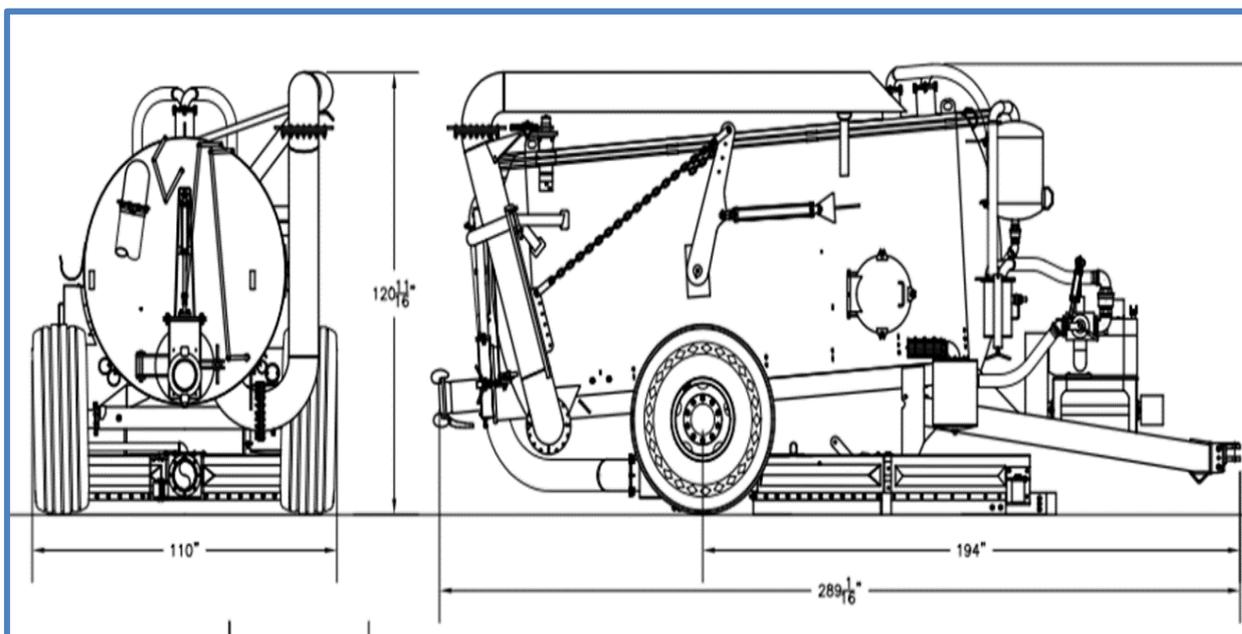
Схема полуприцепной пневматической машины для уборки навоза
